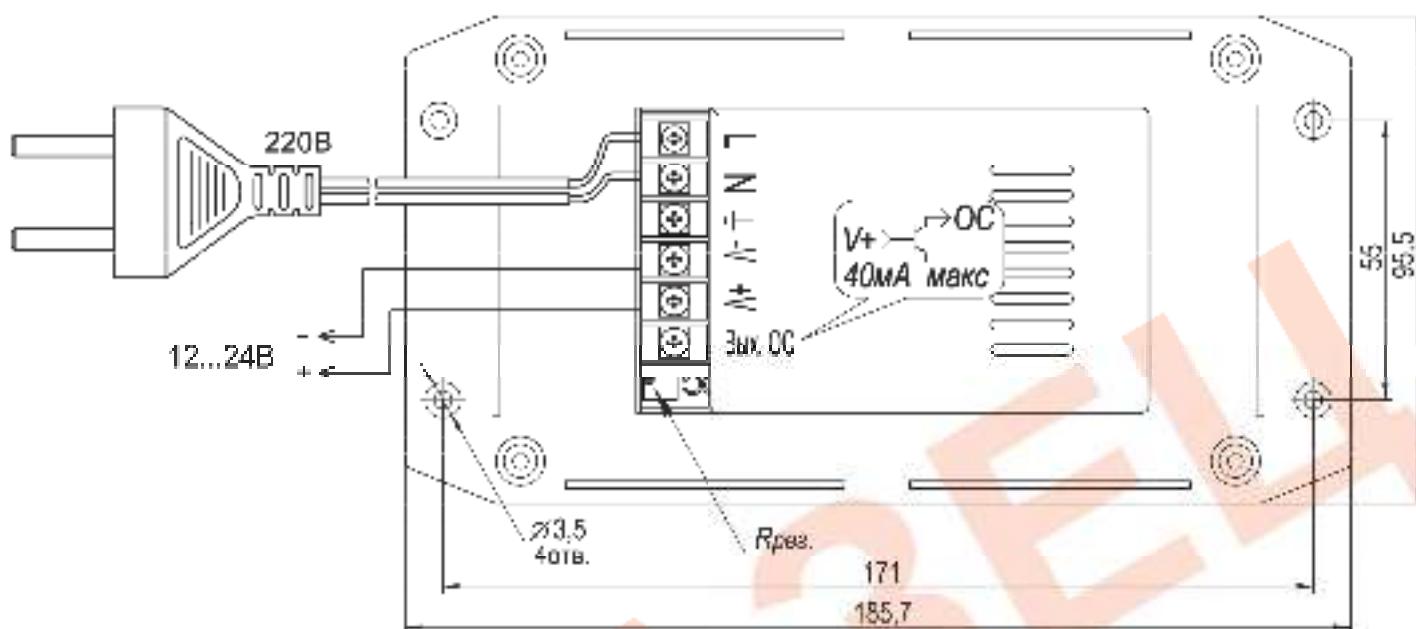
Устройство, габаритные и установочные размеры, подключение изделия
